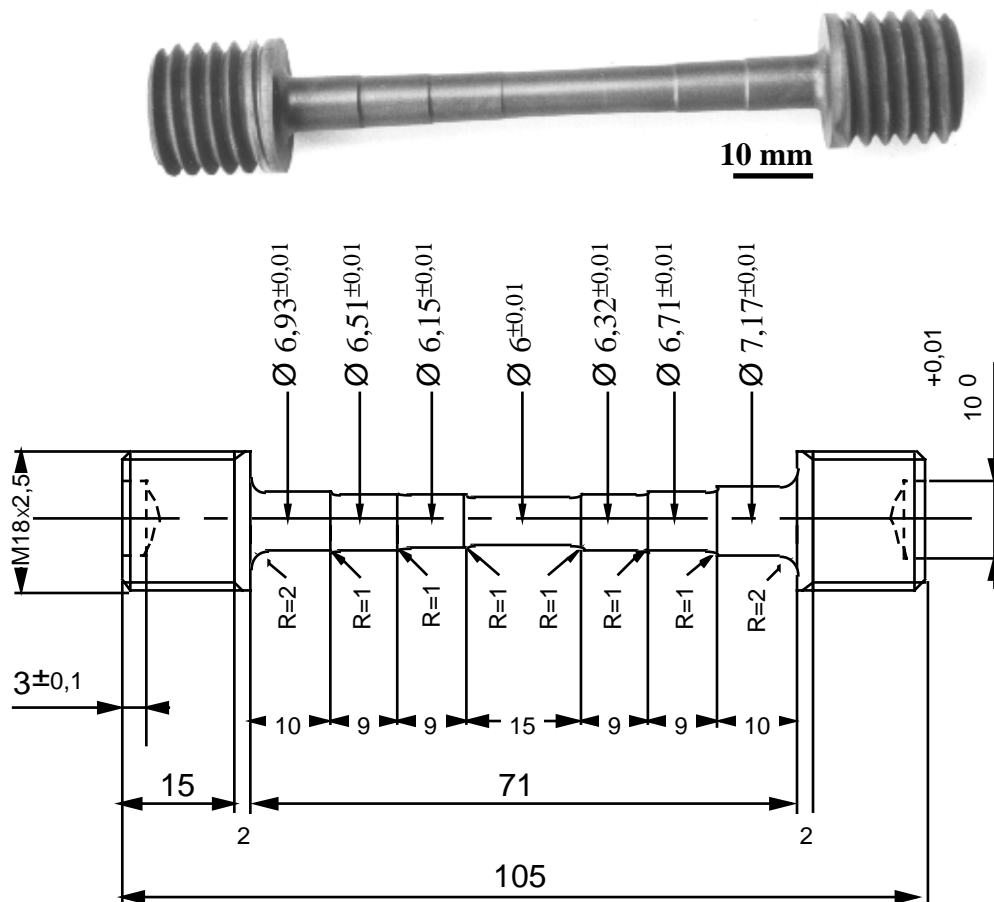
éprouvette multisection Ø6 revêtue par la protection CN22.
